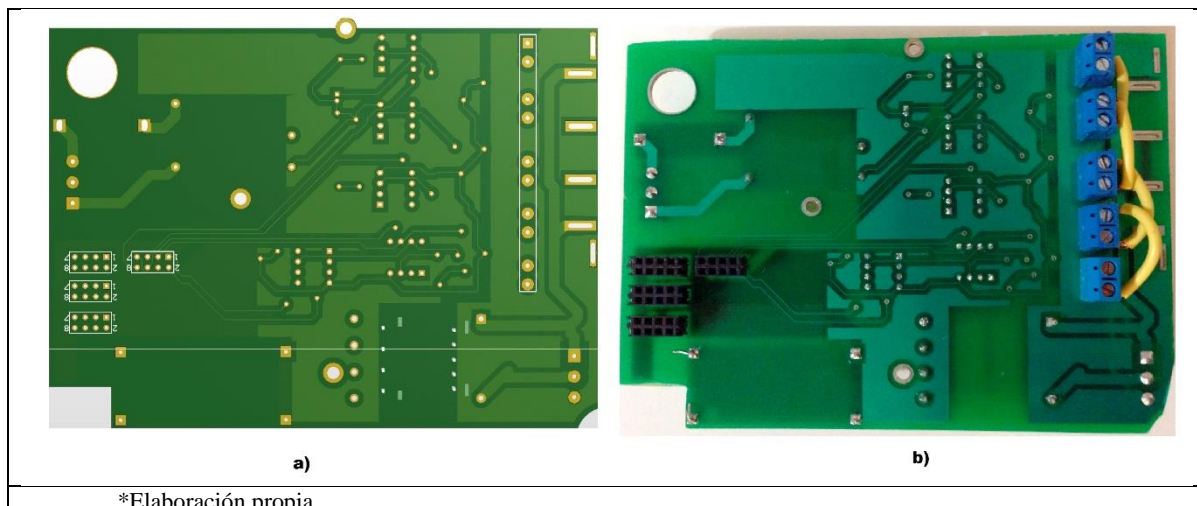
a) Modelo PCB b) Estructura PCB final (vista inferior)
